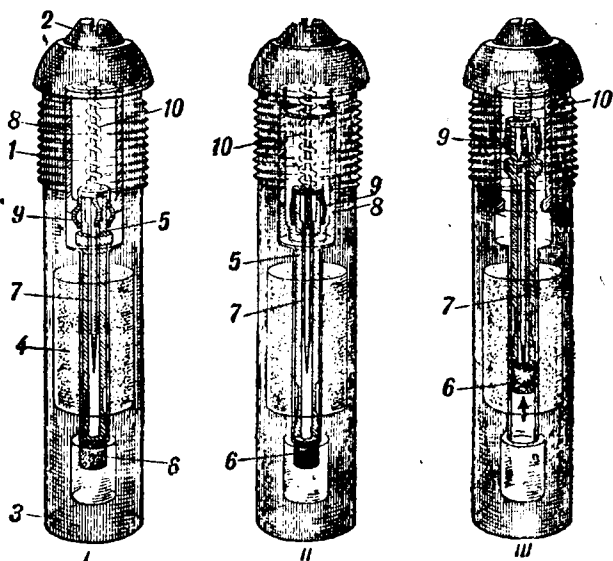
Схема взрывателя УГТ. I — положение подвижных частей взрывателя до выстрела; II — в момент выстрела, III — в момент удара снаряда в преграду; 1 — корпус взрывателя; 2 — головка; 3 — дно; 4 — детонатор (взрывчатое вещество); 5 — уларник; 6 — капсюль; 7 — жало; 8 — оседающий цилиндр; 9 — предохранитель; 10 — пружина.
